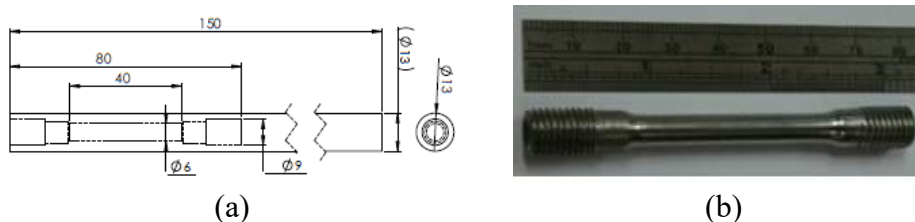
Amostras usadas para ensaio de tração [90]: a) dimensões originais; b) corpo de prova de tração fabricado.
